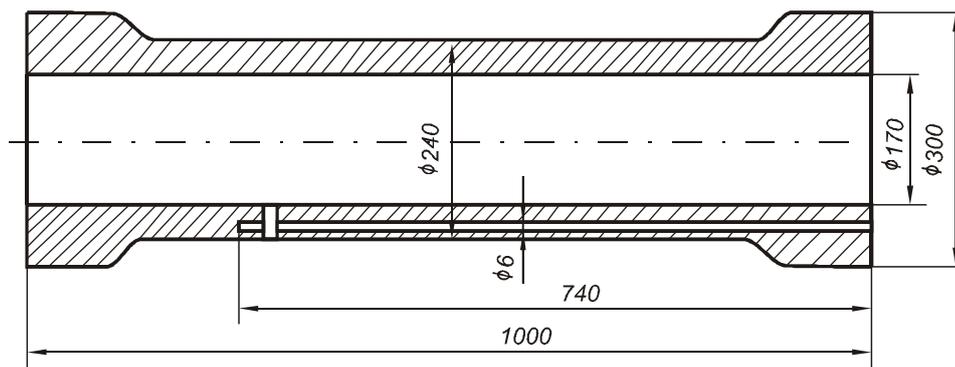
Пример нетехнологичной конструкции корпуса гидравлического цилиндра
